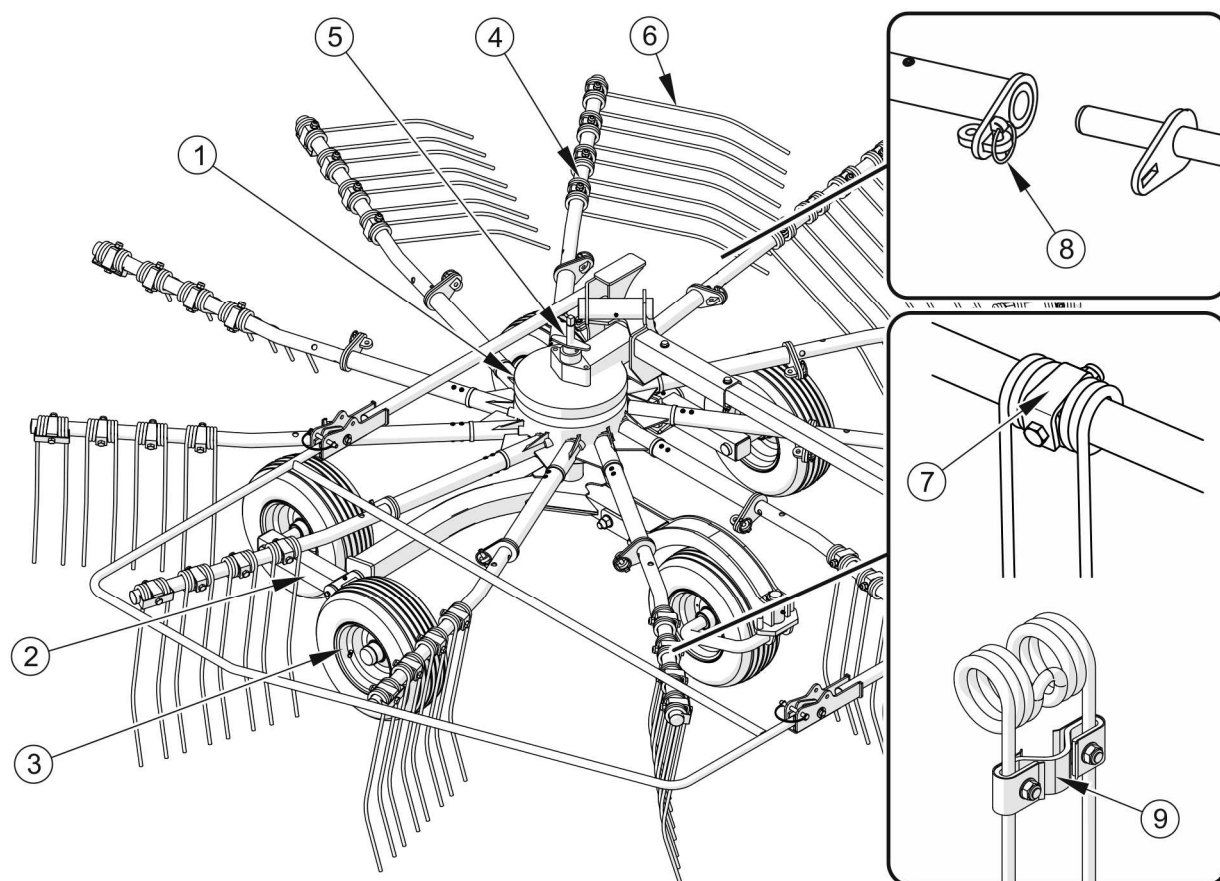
Konstrukce shrnovací soustavy ZKP800
